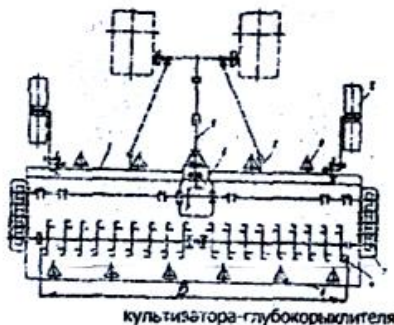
Схема культиватора – глубокорыхлителя фрезерного
